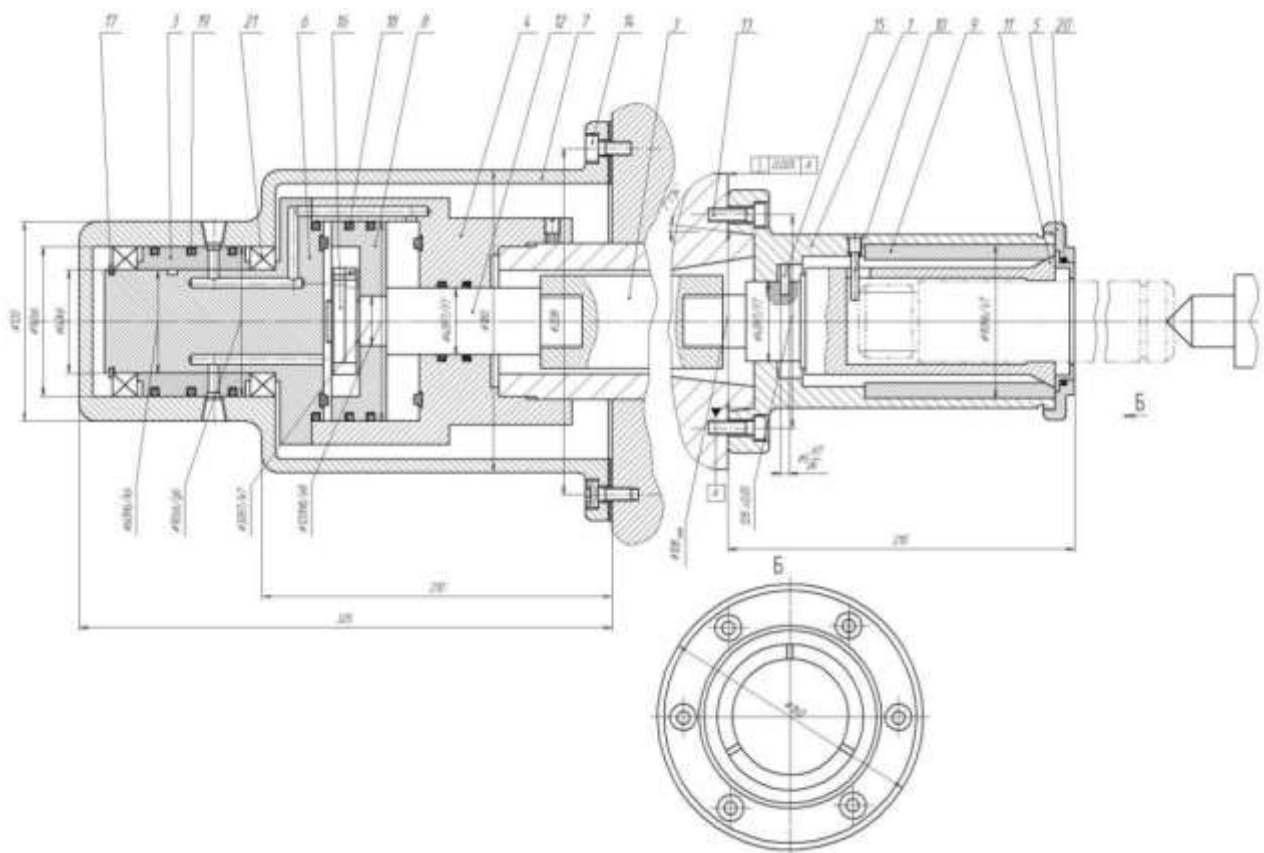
Цанговий патрон для шліцефрезерного верстата
